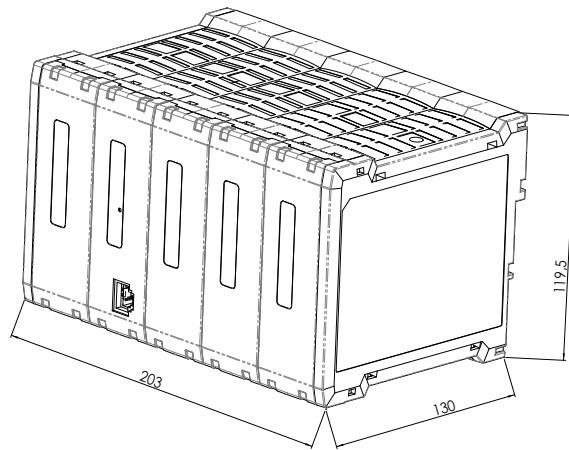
Dimensiones GEDE EDC-T 4I, GEDE EDC-T 4I40.
